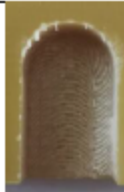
Кінцеве фрезерування за контуром паза фрезою меншого діаметра
